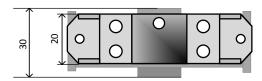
Габаритные размеры устройства для монтажа на рейку DIN. а) вид сбоку
